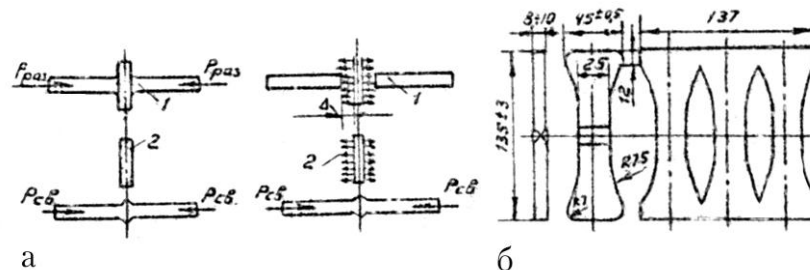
Схемы сварки образцов из термопластических пластмасс:
